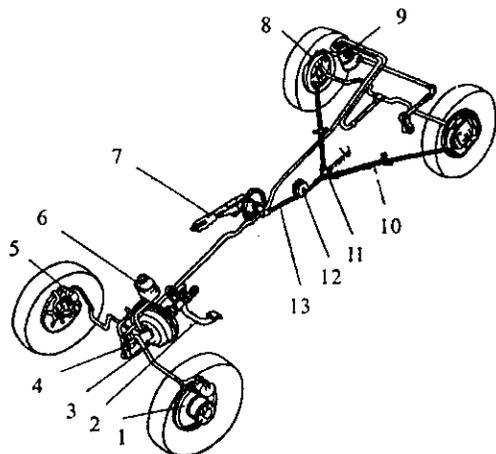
Общий вид тормозной системы автомобиля ВАЗ-2105:
